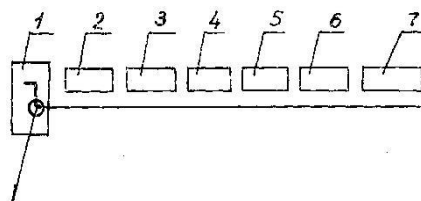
Структурная схема обозначения сварных швов на чертежах по ГОСТ 2.312–72
